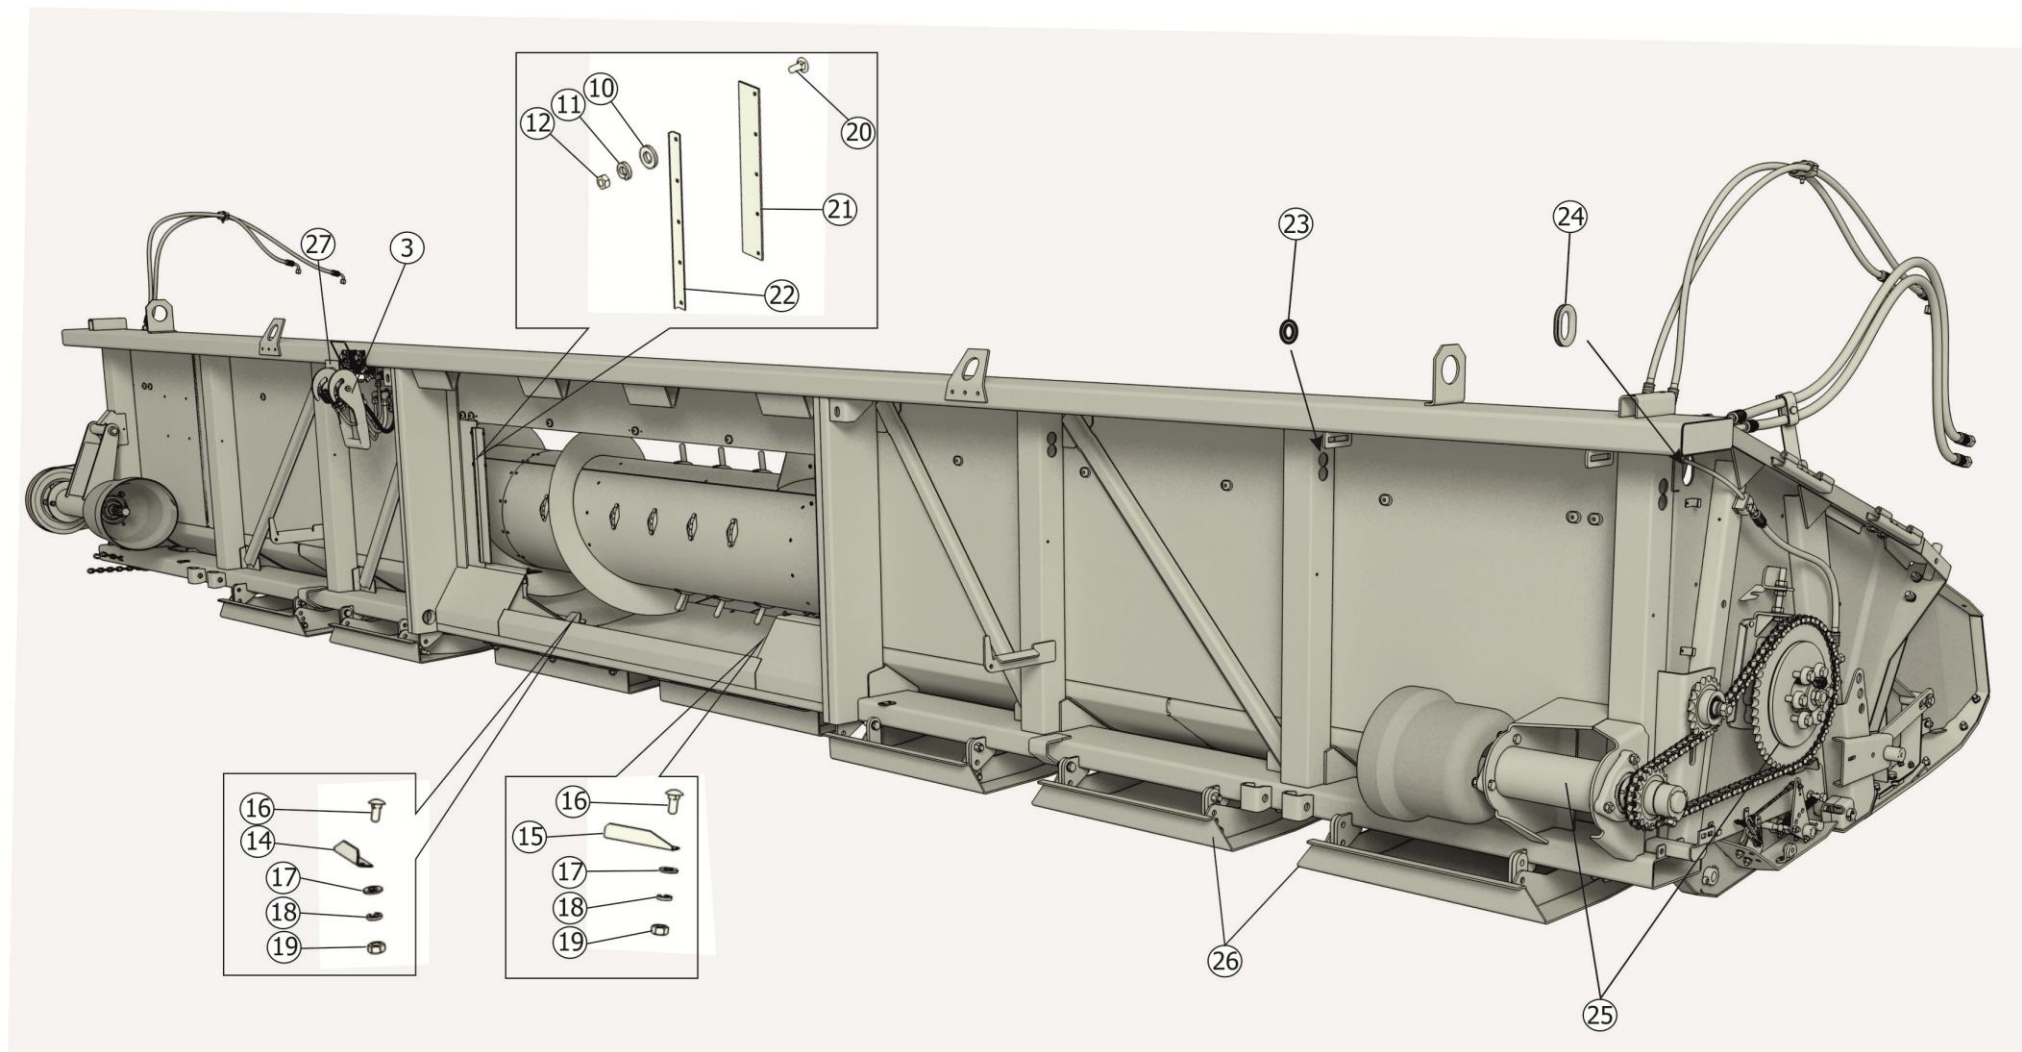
Корпус ЖСУ-704.01.00.000
